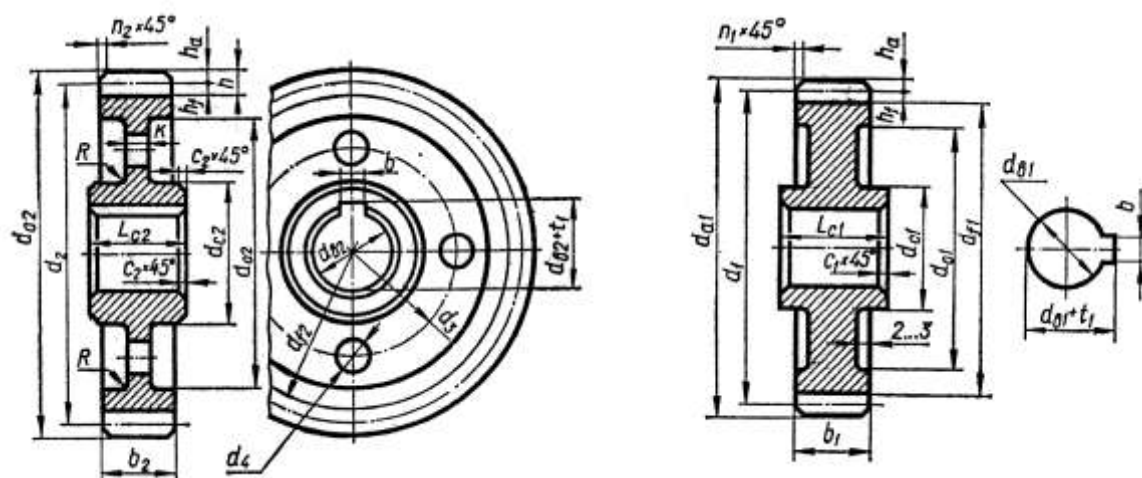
Зображення колеса та шестірні циліндричного зубчастого передавача.
